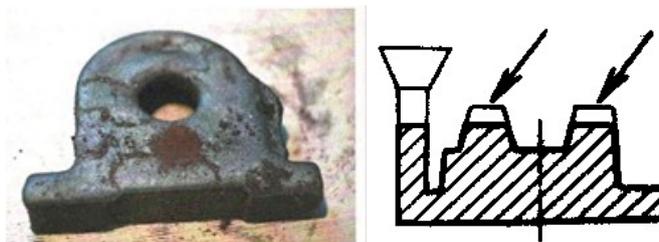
Отливка «Опора» с дефектом «Недолив»
